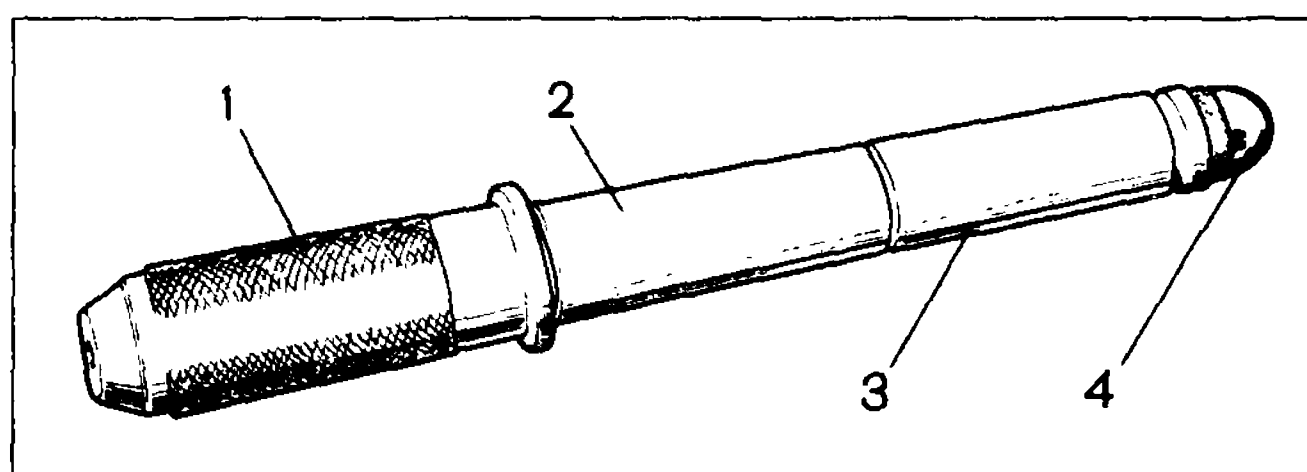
Установка поршневого пальца на приспособление А.60325 для запрессовки его в поршень и головку шатуна: 1 - валик приспособления; 2 - поршневой палец; 3 - направляющая; 4 - упорный винт
